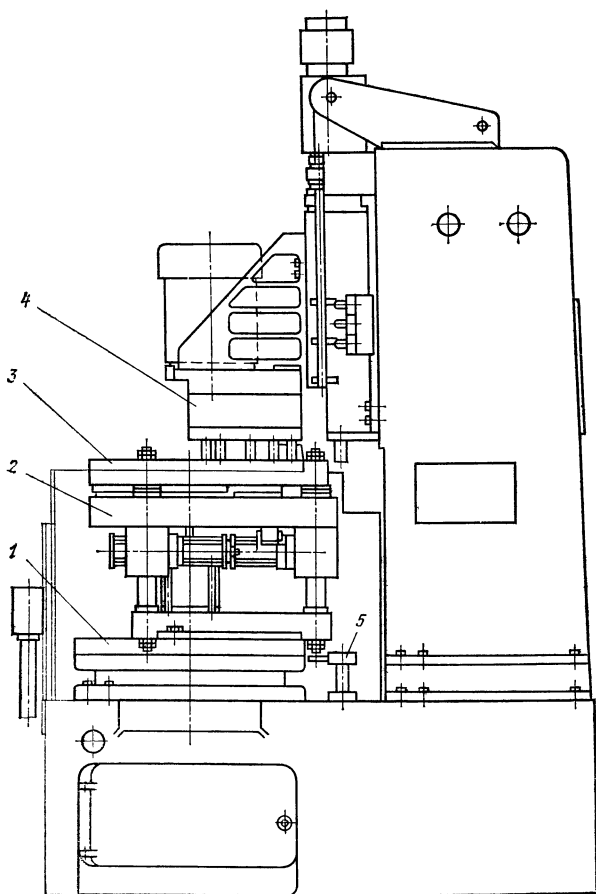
Размещение приспособления с пневмоприводом на агрегатном станке
